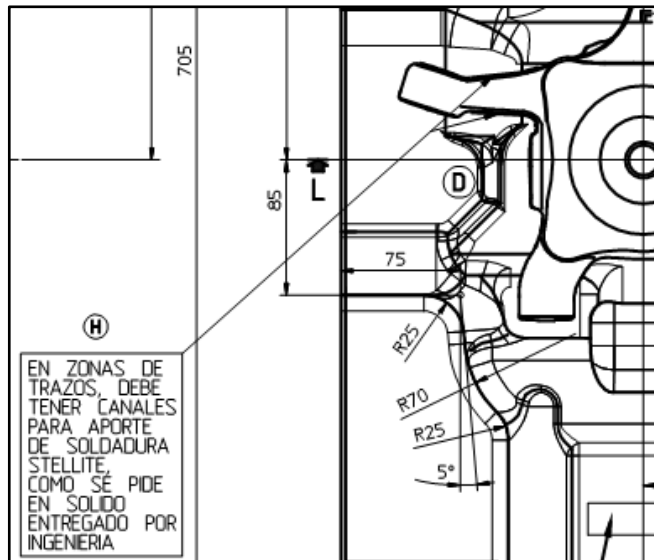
Modificación en plano 2D CRAFMSA de matrices de preformado bajo cambio "H". Fuente: planos CRAFMSA.
